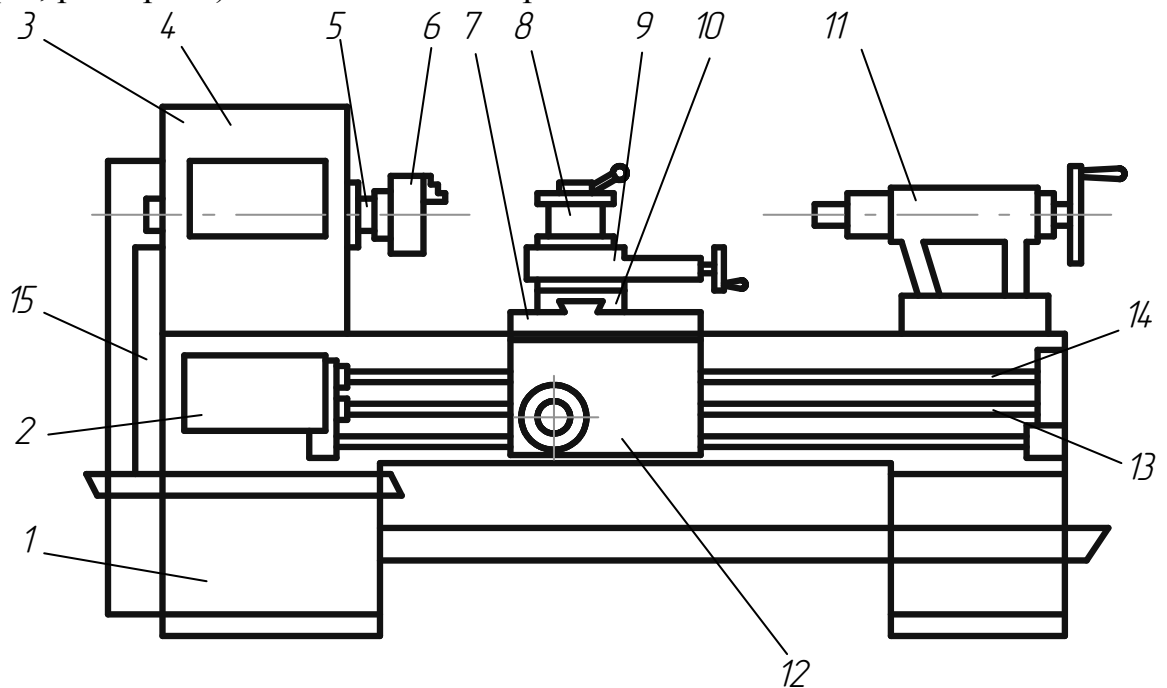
Загальний вигляд токарно-гвинторізного верстата
